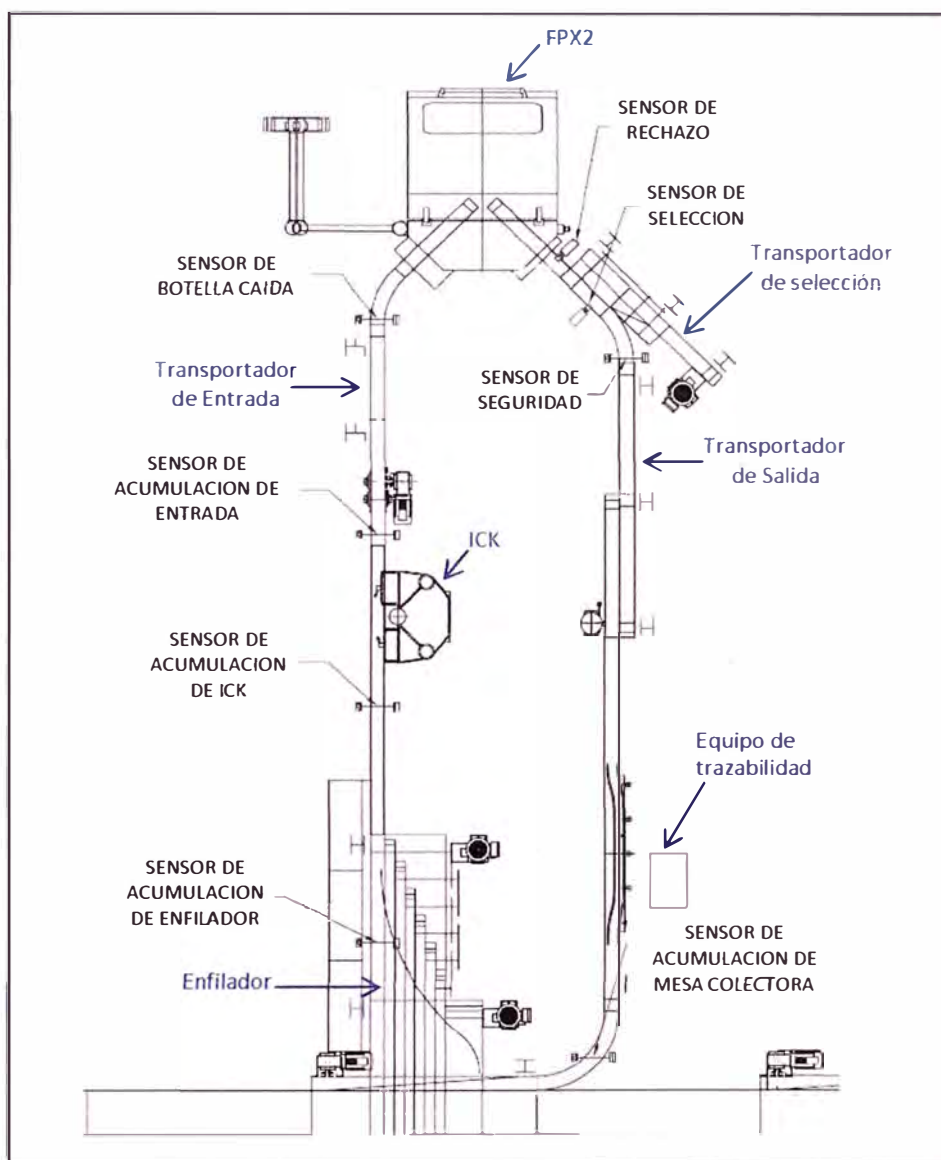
Equipos de una lazo de inspección con FPX2
